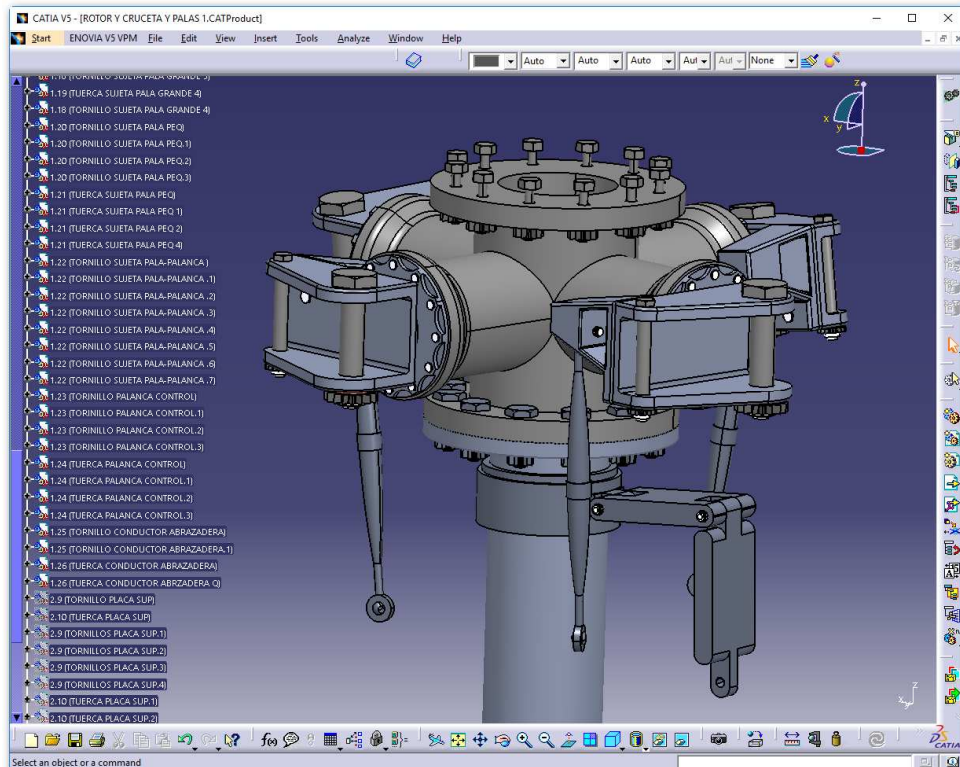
Conjunto cabeza rotor principal sin gorro.
